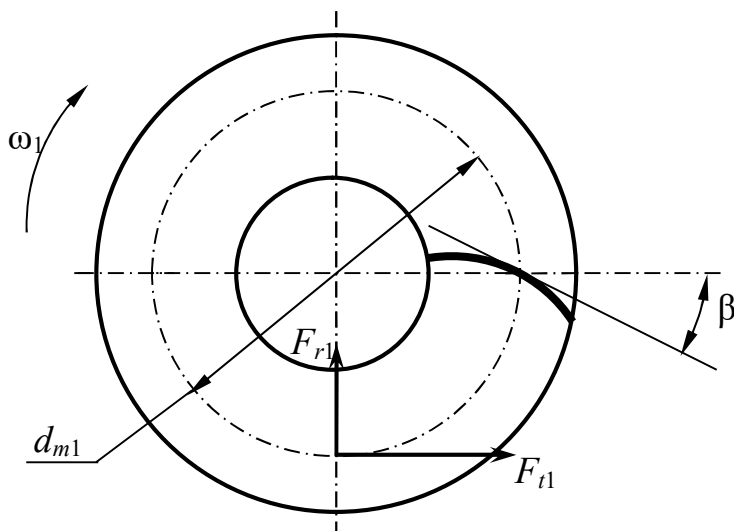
Коническая шестерня с круговым зубом (вид со стороны вершины конуса)
